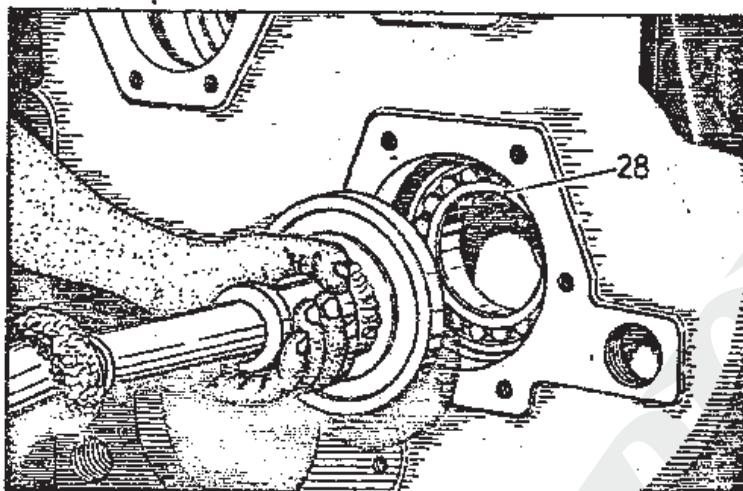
Вдавливание бочкообразного роликоподшипника 22217 в гнездо внутри корпуса коробки скоростей с помощью стержня.
